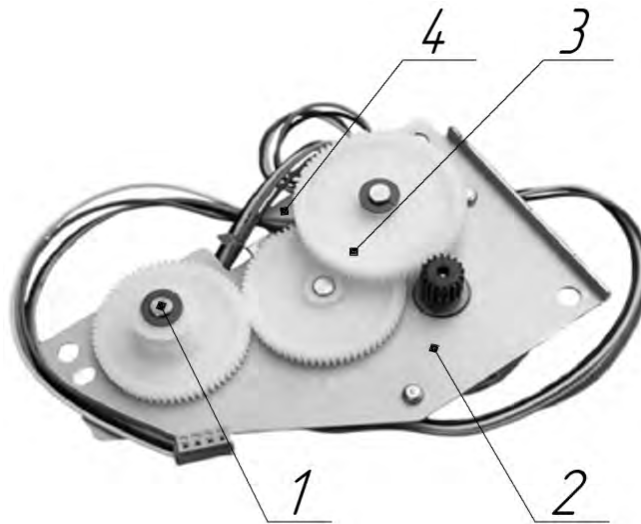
Двигатель сканера с редуктором в сборе для МФУ Canon MP140: 1 – направляющая ось; 2 – направляющая пластина; 3 – редуктор; 4 – электродвигатель
